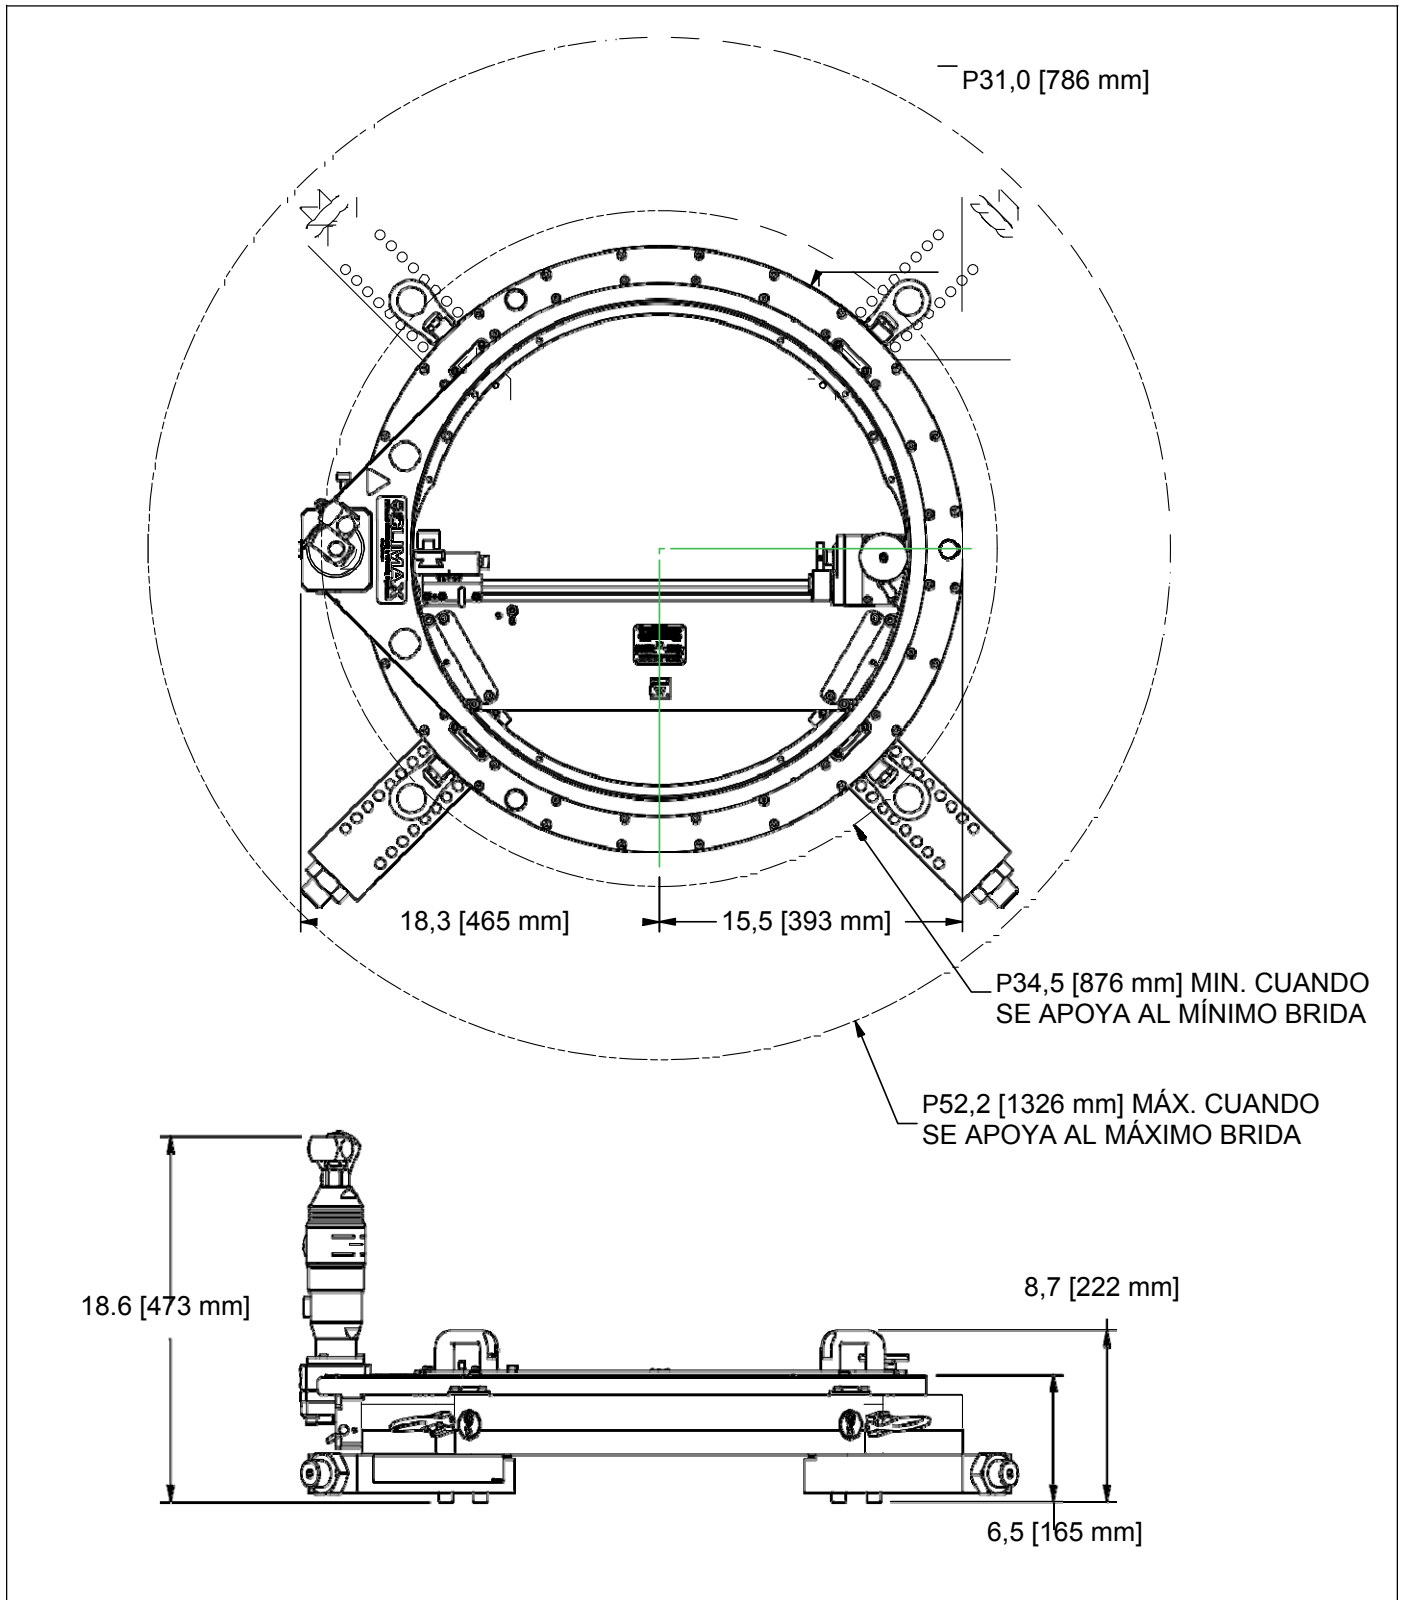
FF2400 DIMENSIONES DE LA MÁQUINA
